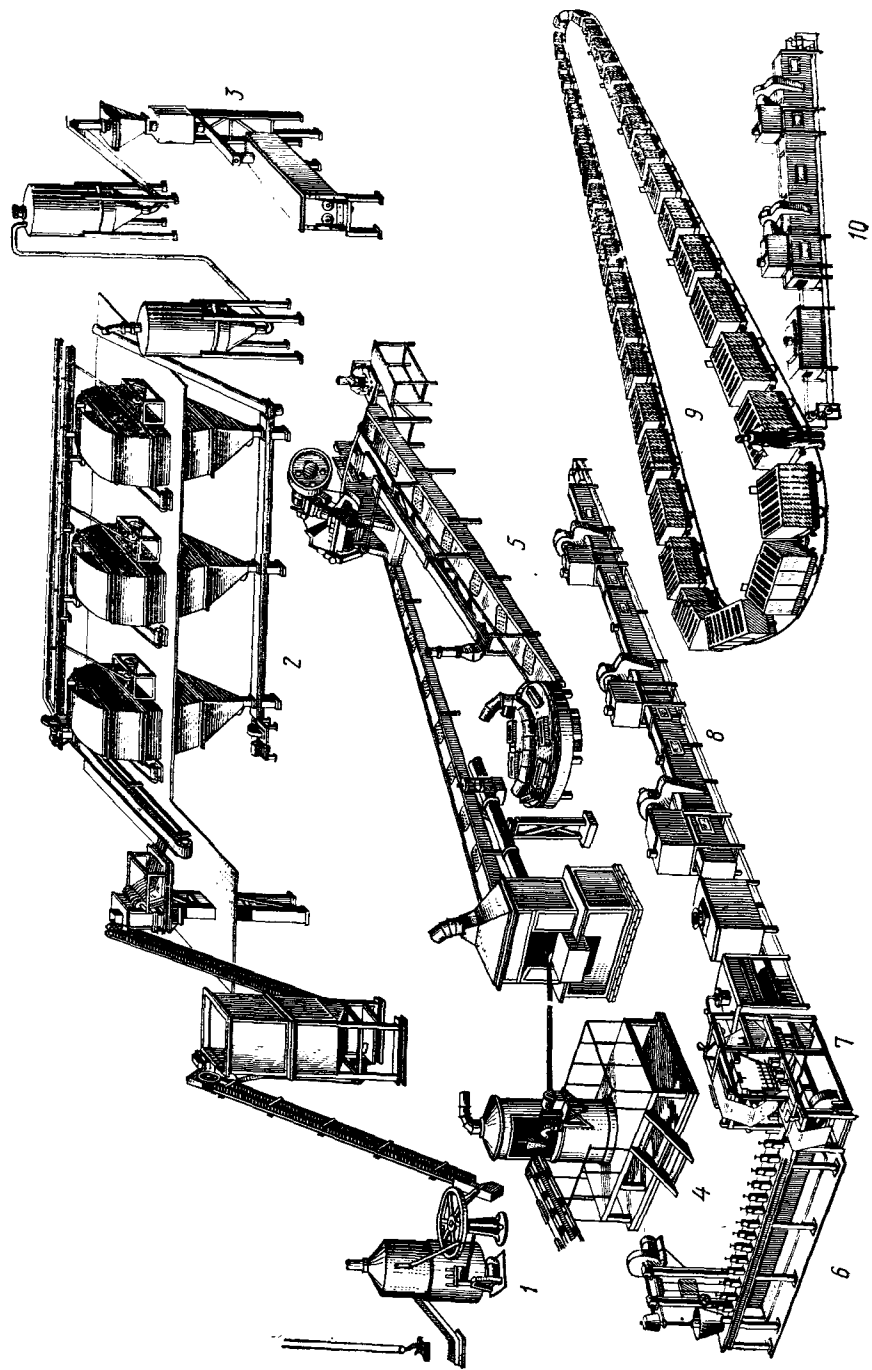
Механизированная поточная линия по производству свинцово-кислотных аккумуляторов: 1 — отливка свинцовых шариков, 2 — получение свинцового порошка, 3 — изготовление пасты, 4 — изготовление намазки пластин, 5 — прокатка пластин, 6 — прокатка пластин, 7 — прокатка пластин, 8 — сушка свеженамазанных пластин, 9 — формирование пластин, 10 — сушка отформированных пластин
